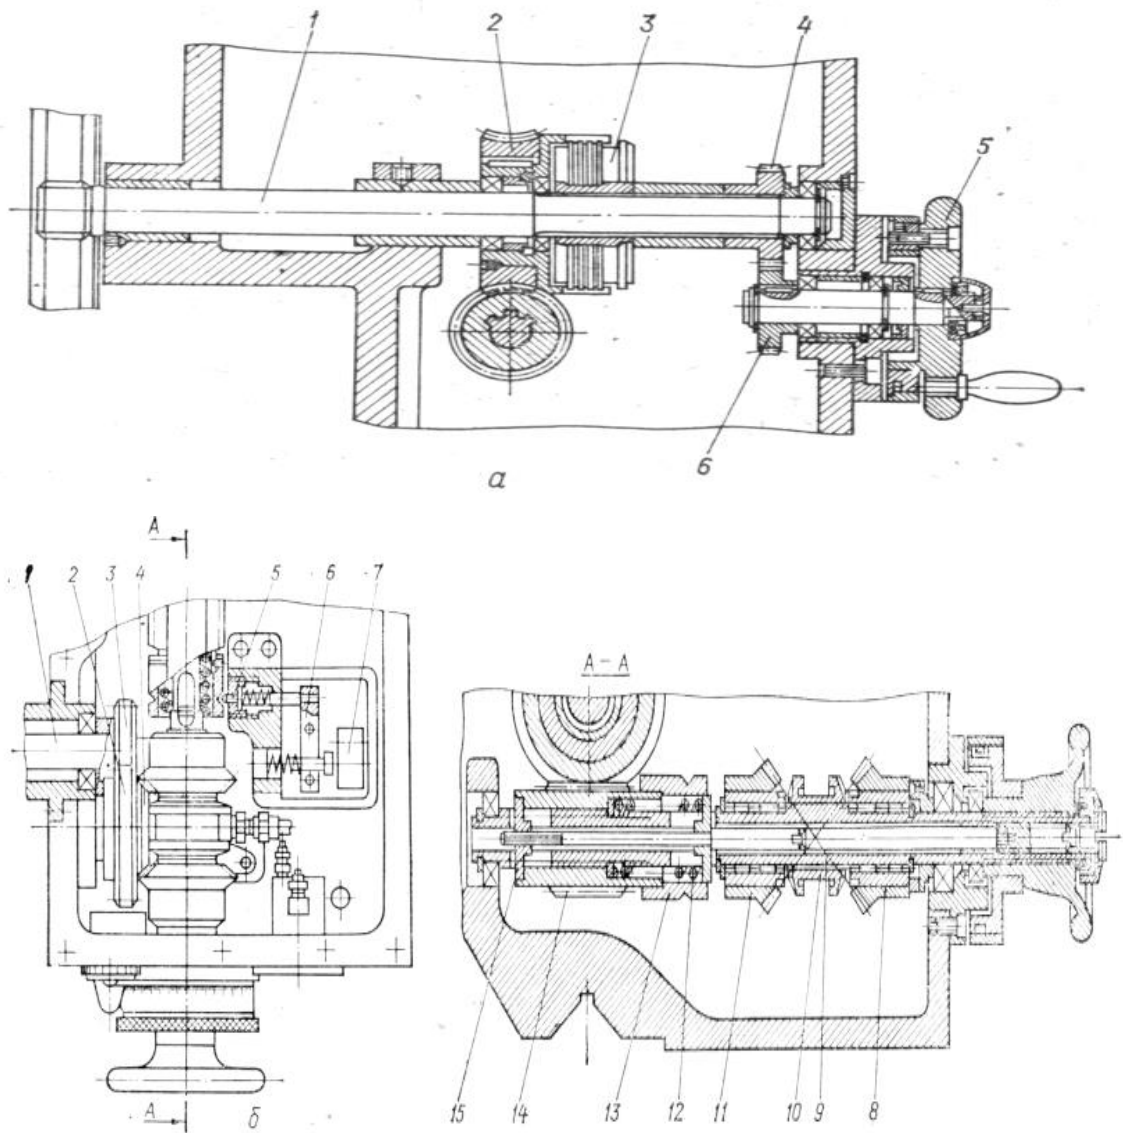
Приводи ручного обертання (а) і автоматичної кругової подачі (б) револьверної головки верстата мод. 1Г340П
